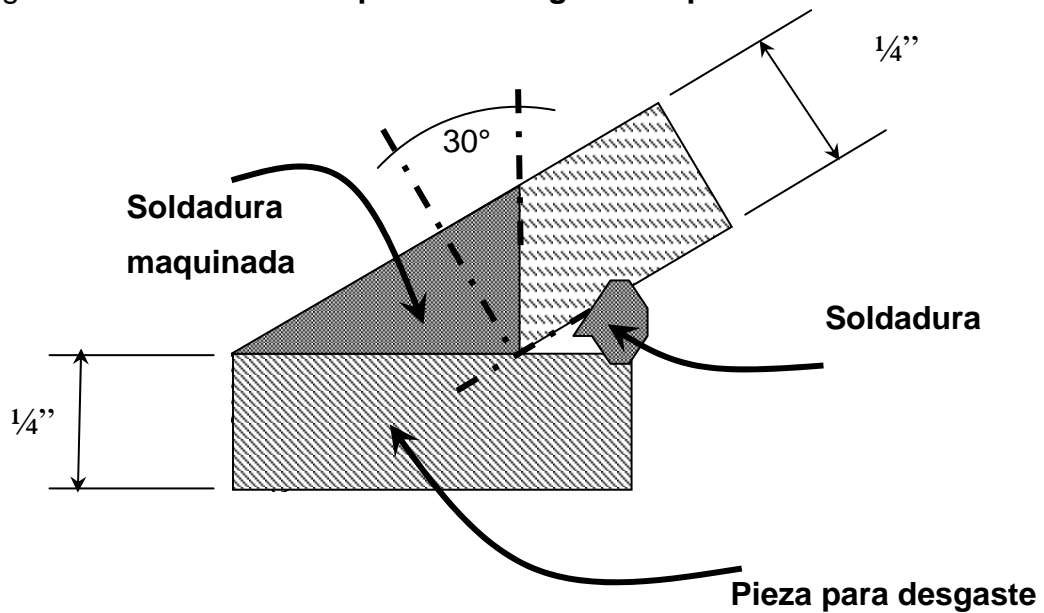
Soldadura de pieza de desgaste en protector de cadenas
